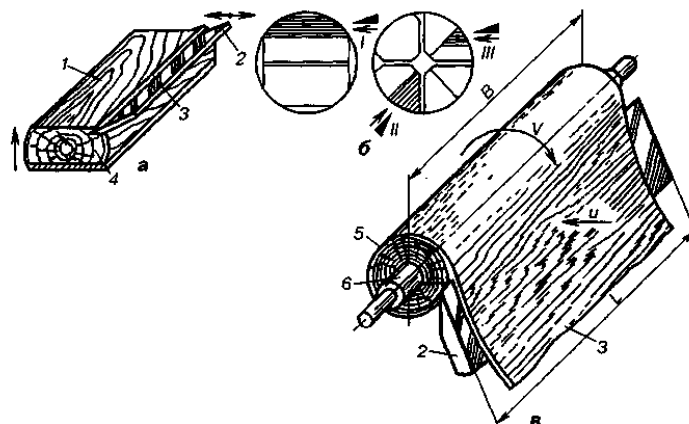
Способи отримання шпону: а - струганням; б - обробкою окоренка для одержання шпону тангенціального (I), радіального (II), напіврадіального (III); в-луцненням; 1 - заготовка; 2 - ніж; 3 - шпон; 4 - відструг; 5 - колода; 6 - кулачок
